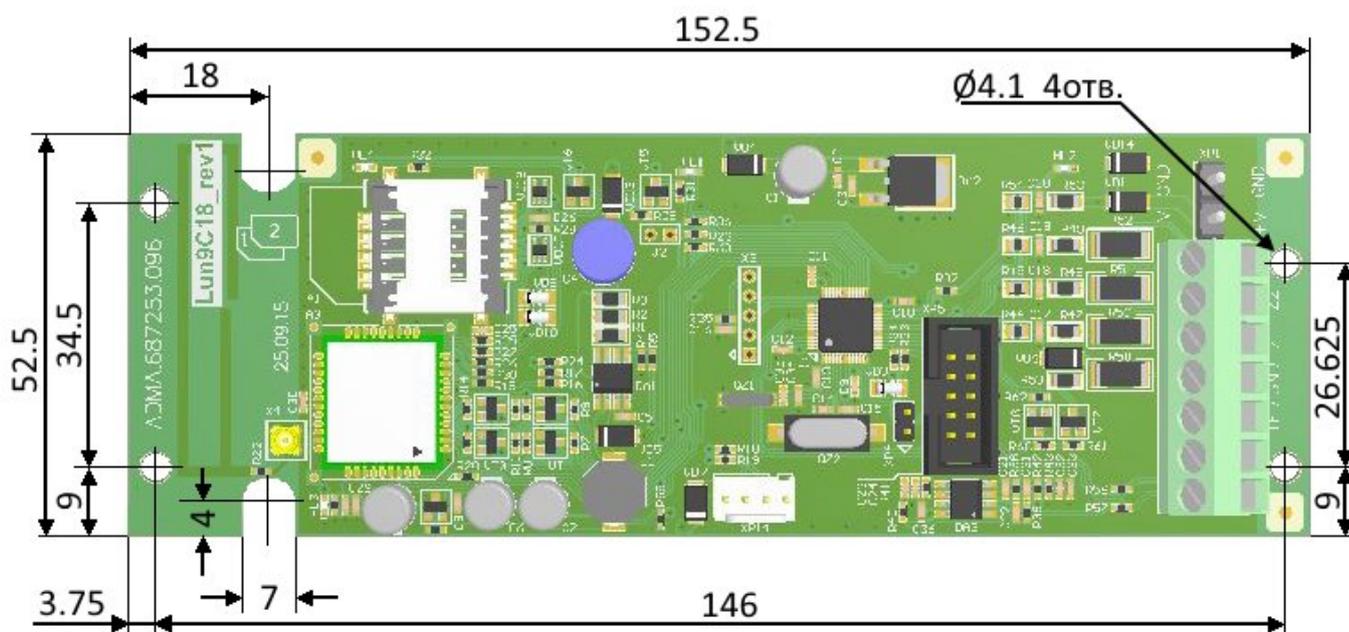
Габаритные и присоединительные размеры платы УСО
